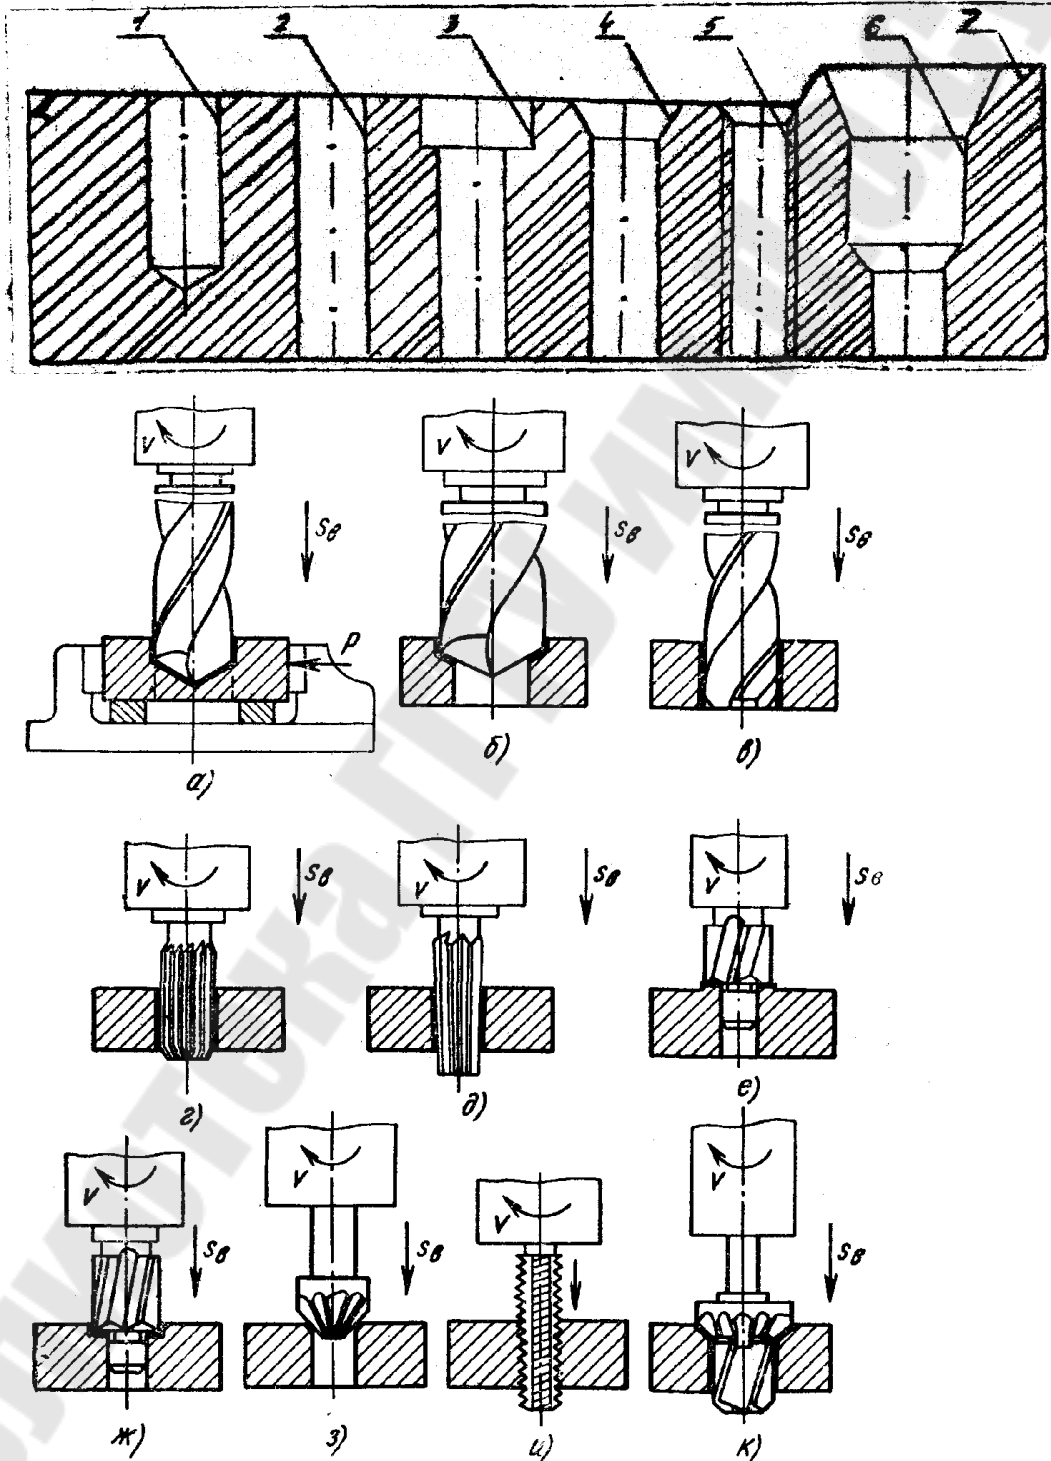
Схемы обработки на вертикально-сверлильных станках
